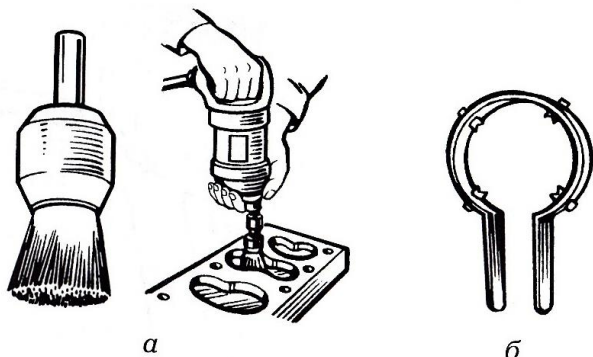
Приспособления для удаления нагара из головки цилиндров (а) и канавок поршней (б)
